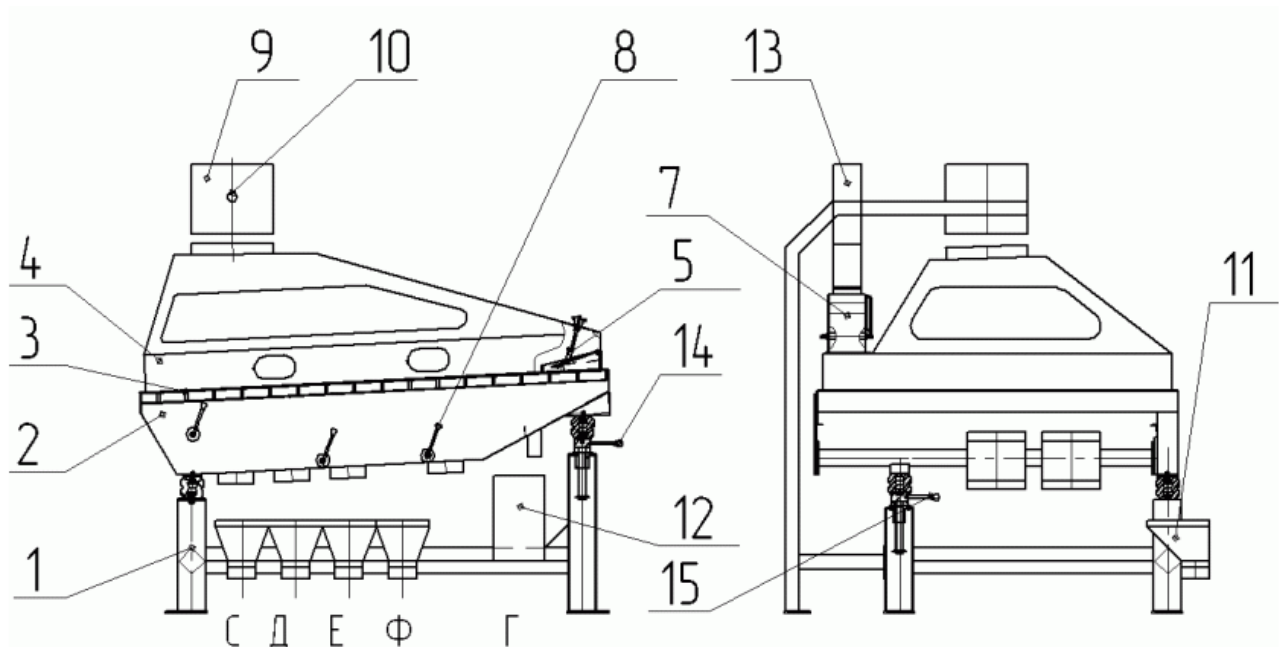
Конструктивна схема ПСС: 1 – станина; 2 – вібростіл; 3 – кузов; 4 – камера аспіраційна; 5 – каменевідбірник; 6 – дека; 7 – живильник; 8 – клапан регулювальний; 9 – клапан повітряний; 10 – механізм регулювання витрати повітря; 11 – патрубки вивантажувальні; 12 – ємність для каменів; 13 – патрубок завантажувальний; 14 – механізм регулювання повздовжнього кута нахилу; 15 – механізм регулювання поперечного кута нахилу; С – фракція легка; Д – фракція середня; Е – фракція змішана; Ф – фракція важка; Г – каміння
